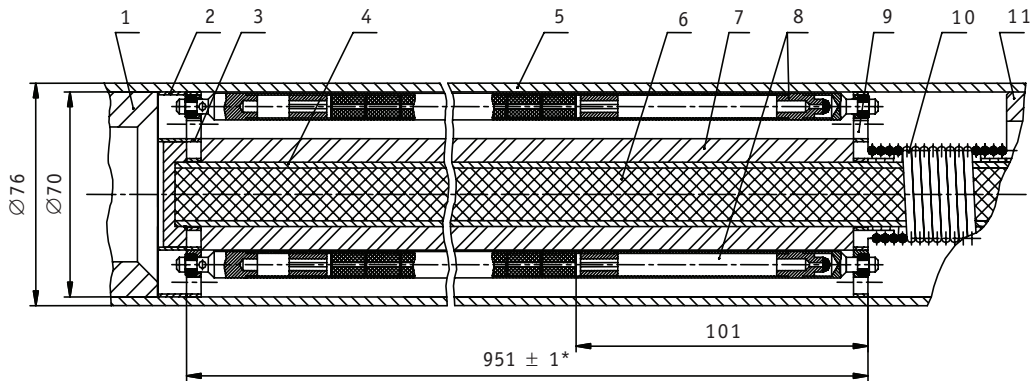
Продольный разрез ТК реактора ИВГ1.2М в районе активной зоны: 1 – втулка биологической защиты; 2 – нижняя опорная решетка; 3 – нижняя решетка; 4 – труба для установки поглотителя нейтронов; 5 – корпус ТК; 6 – поглотитель нейтронов; 7 – бериллиевый вытеснитель; 8 – твэл; 9 – верхняя опорная решетка; 10 – пружина; 11 – втулка упорная
